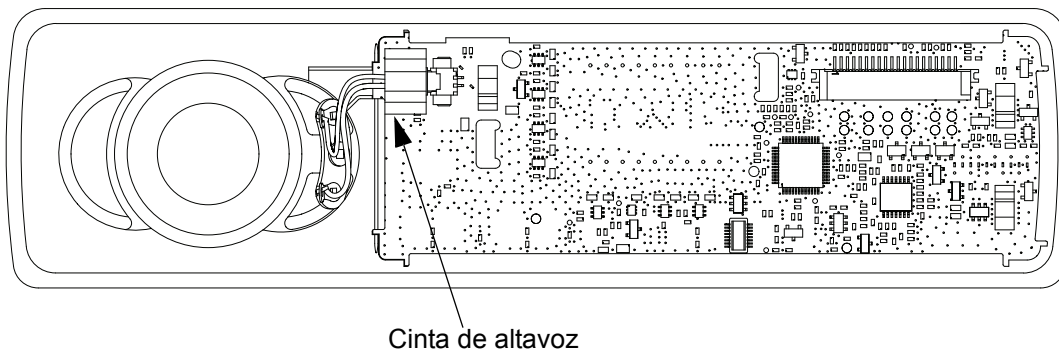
Montaje de la cinta del altavoz en la PCB
